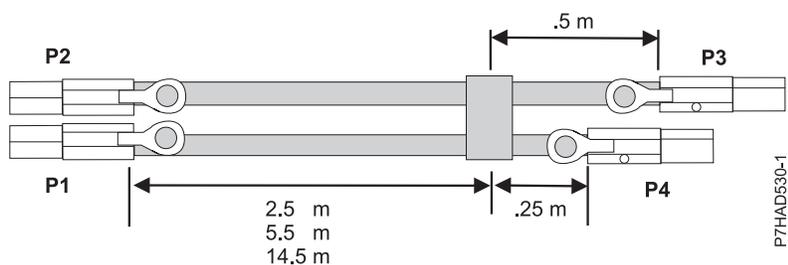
Comprimentos de cabos de montagem de cabo X externo SAS
